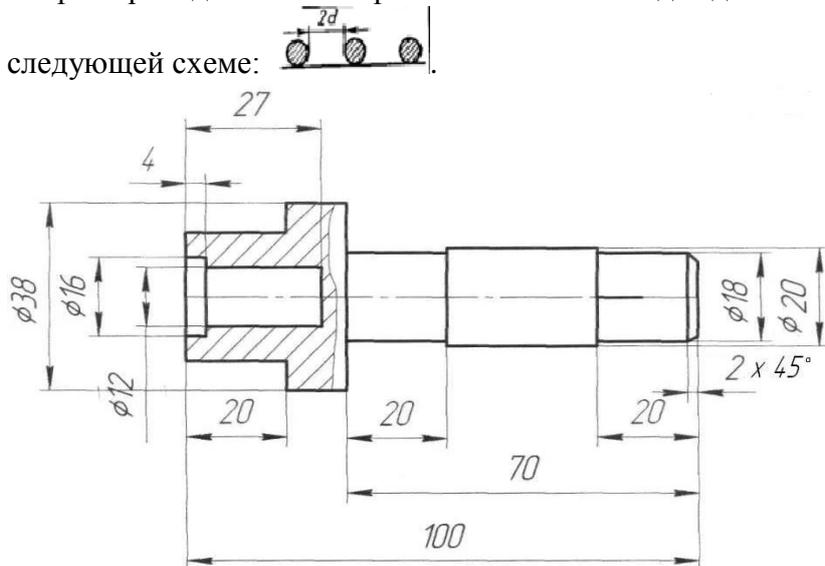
Эскиз детали «Вал ведущий», материал – сталь 40Г2.
